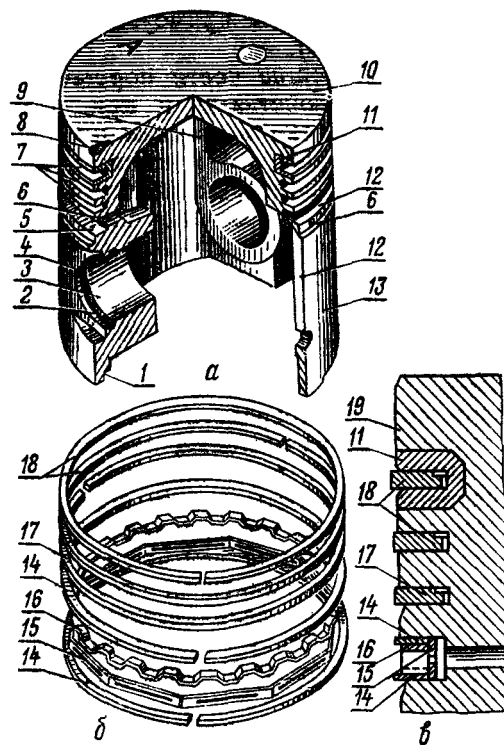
Поршень и поршневые кольца двигателя ЗИЛ-130:
